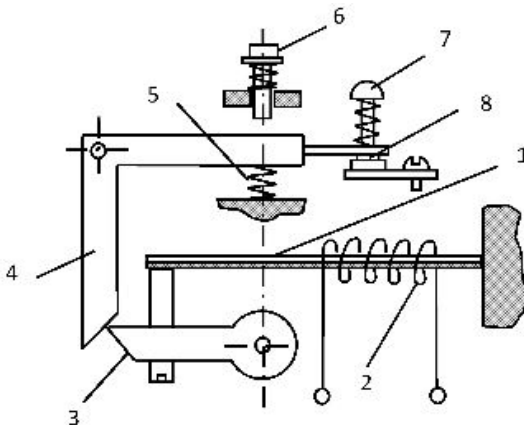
Конструкція теплового реле з розчіплювачем із безпосереднім нагрівом: 1 – біметалева пластинка; 2 – нагрівальний елемент; 3 – засувка; 4 – важіль; 5 – пружина; 6 – кнопка; 7 – регулювальний гвинт; 8 – контакти
